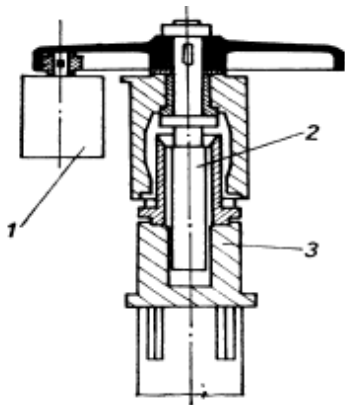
Typy vřetenových poháněcích mechanismů [103]
